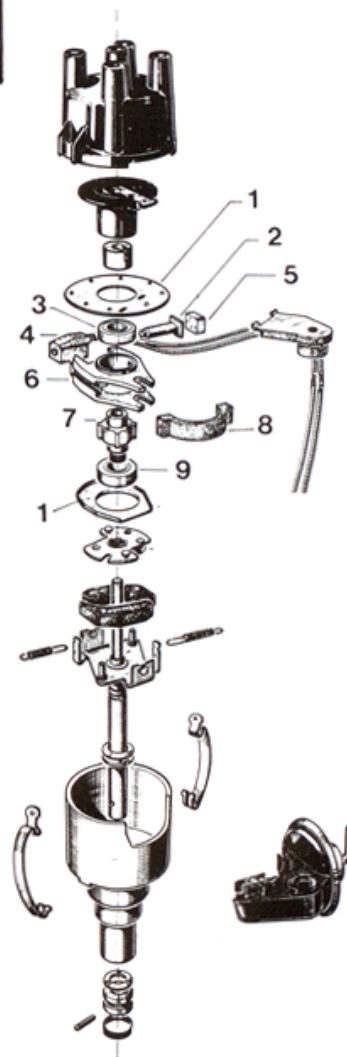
Despiece general de un delco provisto de captador magnético. 1, pantalla magnética. 2, núcleo. 3, cojinete. 4, bobina. 5, imán. 6, estator. 7, rueda polar. 8, zona de estanqueidad. 9, cojinete.
